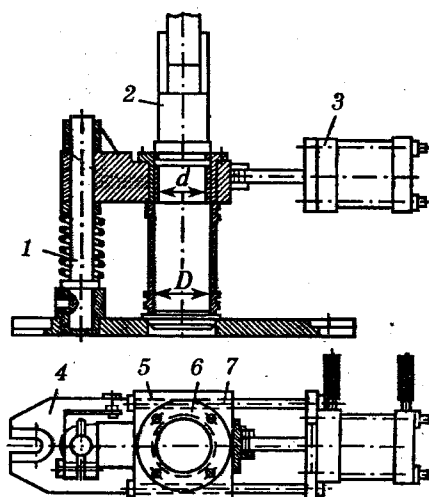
Приспособление для совмещения операций свертывания и запрессовки пластины в гильзу цилиндров:
